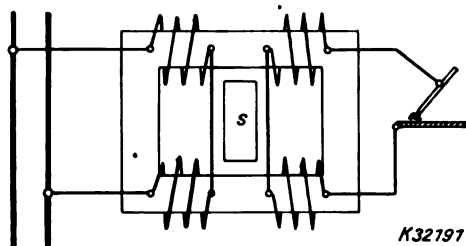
Prinzipbild des Schweißumspanners.
